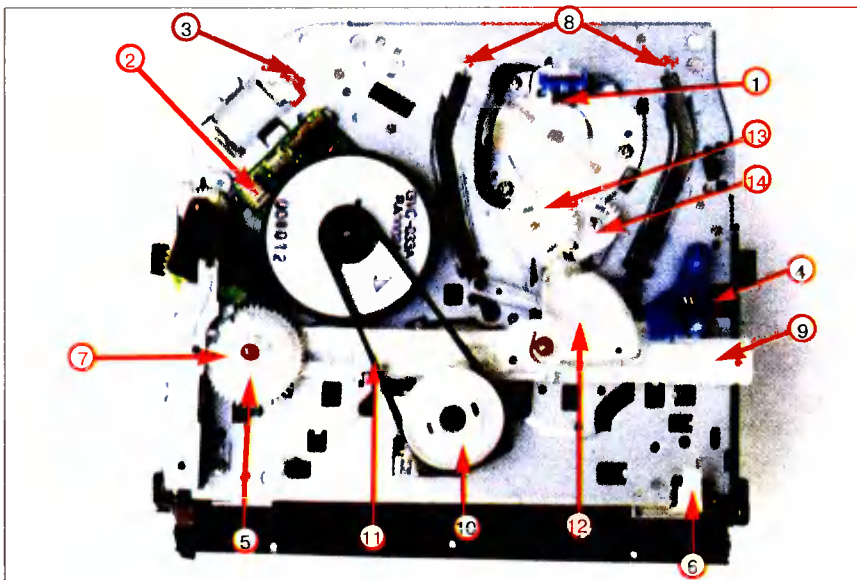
1 — разъем видеоголовок; 2 — разъем ведущего двигателя; 3 — разъем двигателя заправки; 4 — разъем стирающей головки; 5 — гнездо для поводка программного переключателя; 6 — рычаг блокиратора записи; 7 — программная шестерня; 8 — упоры узлов направляющих стоек; 9 — программная планка; 10 — узел подмотки; 11 — ремень привода; 12 — секторная шестерня; 13, 14 — шестерни заправки
